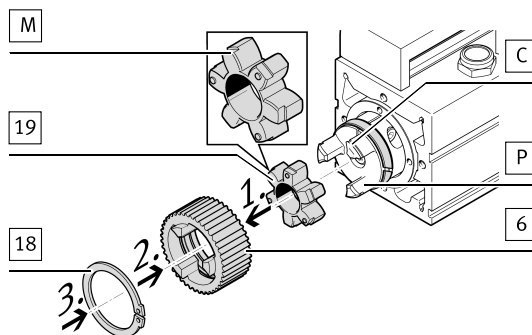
Крепление шкива зубчатого ремня на стороне координатного привода
